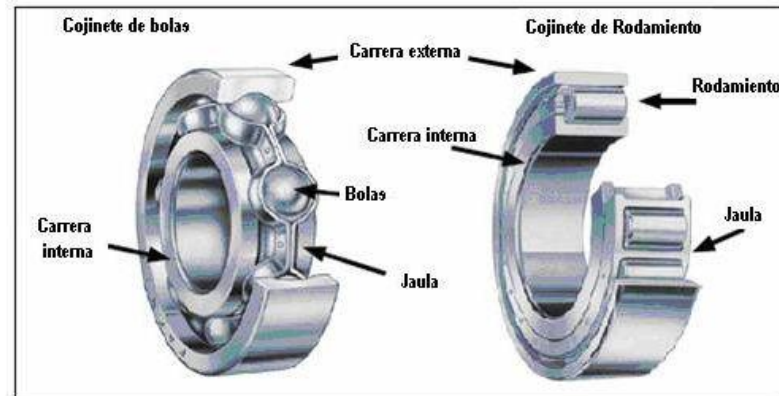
COMPONENTE DEL MOTOR – COJINETE
